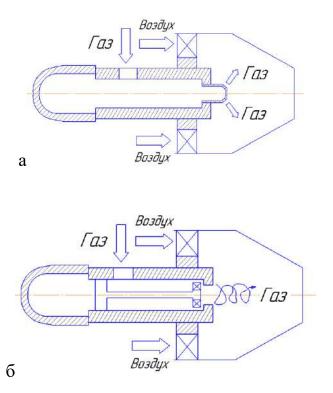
Схема форсунки а) Струйная форсунка б) форсунка с подачей закрученной топливной струи
